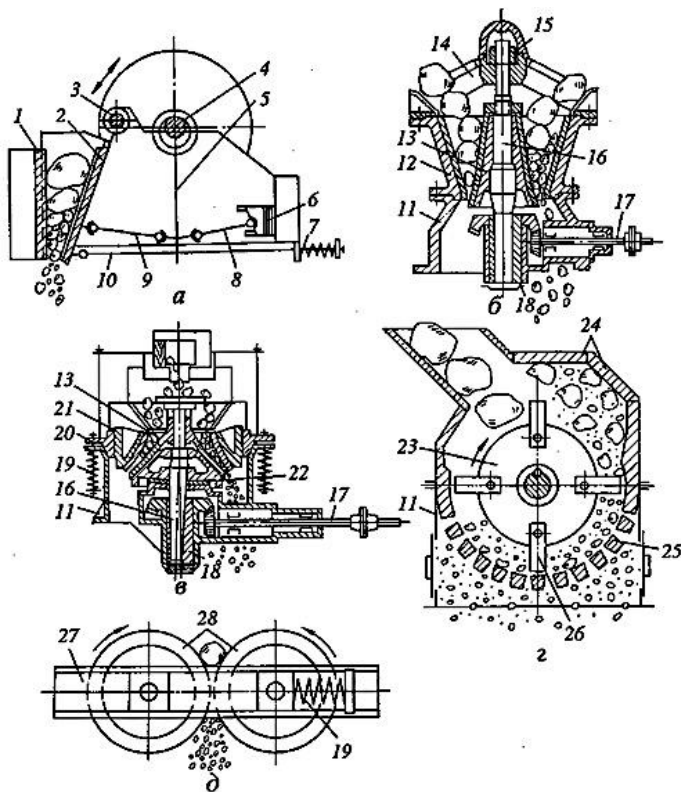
Конструктивные схемы дробилок [12]:
